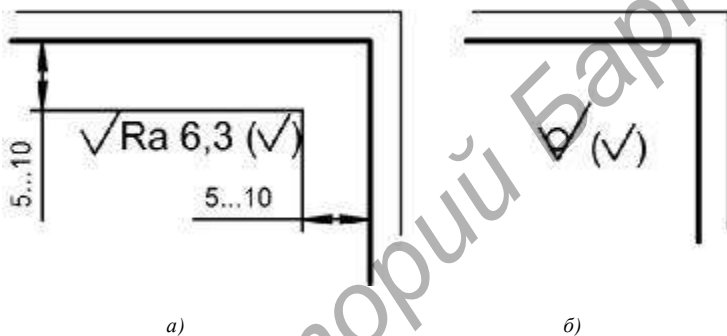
Обозначение преобладающей шероховатости поверхностей детали
